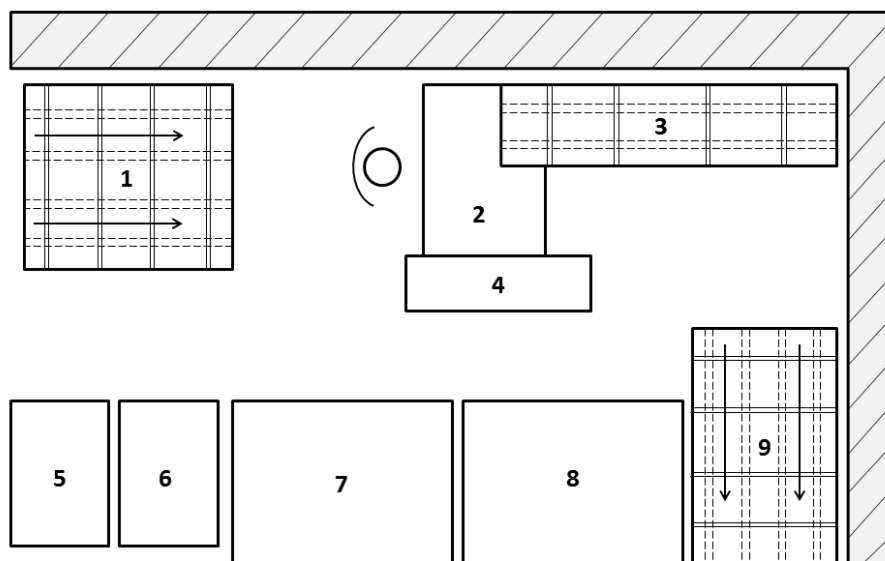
Layout* do posto de pré montagem do *rear heater
